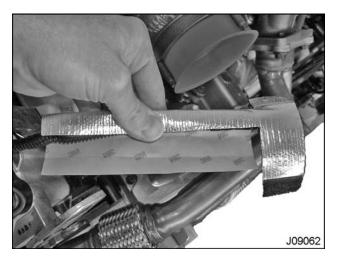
Blindage réfléchissant sur le faisceau de câblage
